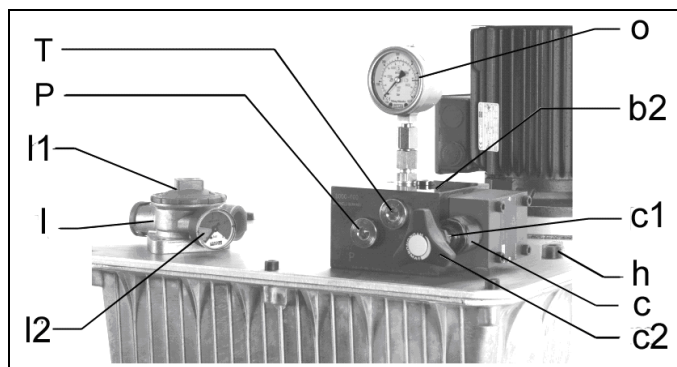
Pumpenaggregat mit Anschlussblock und Rücklauffilter
